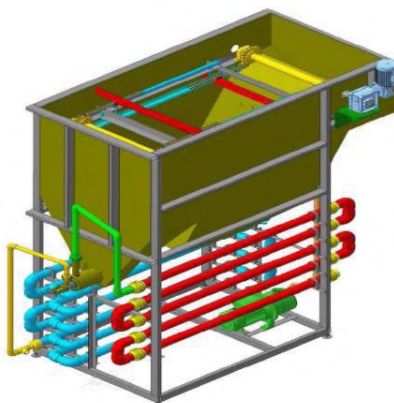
Напорный реагентный флотатор НРФ-2
